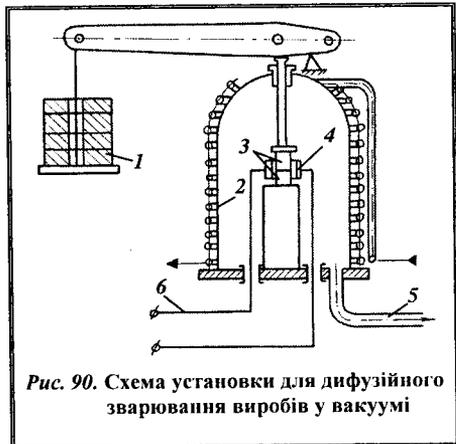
Схема установки для дифузійного зварювання виробів у вакуумі
